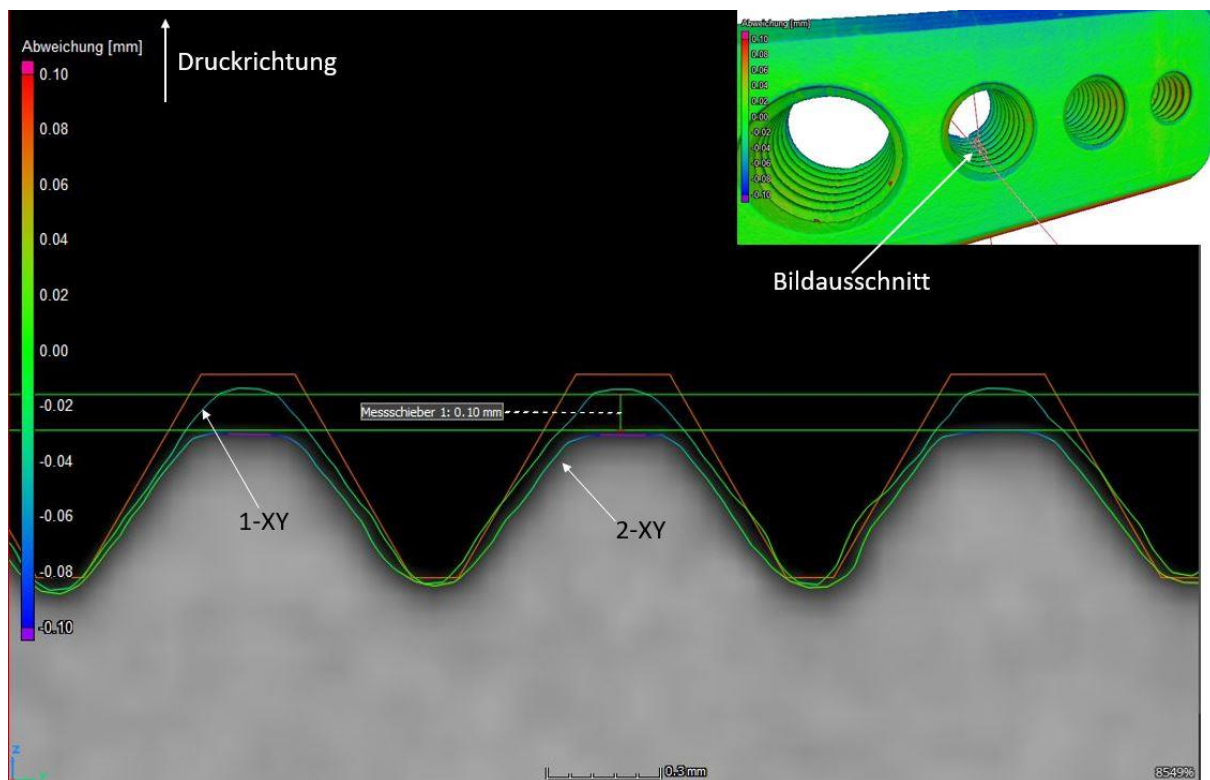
Detail Ansicht M6 Proben 1-XY und 2-XY. Liegende Gewindeflanke
